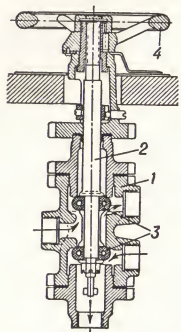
Вентиль-переключатель для перемены направления двух потоков: 1 — корпус; 2 — шток; 3 — резиновые клапаны; 4 — штурвал.
